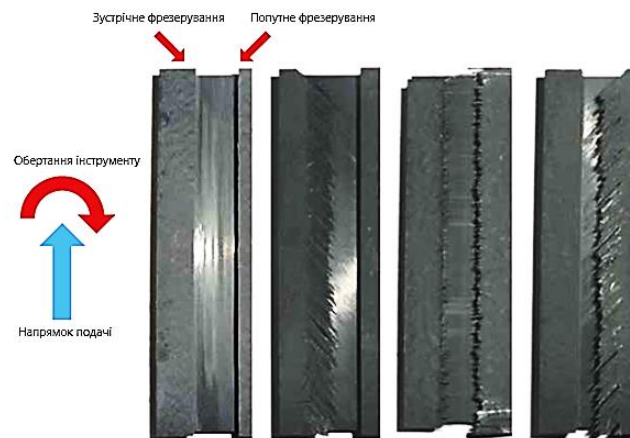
Результати фрезерування полімерних композитів з кутами укладання волокон 0° , 45° , 90° , 135° [22]
